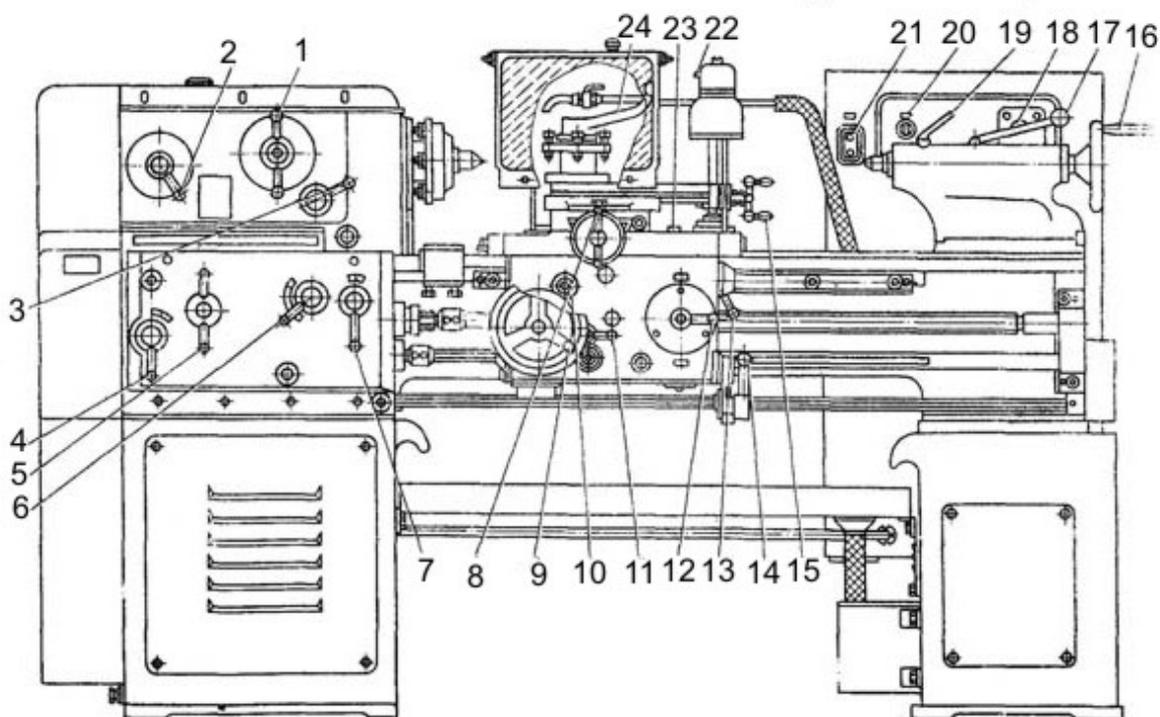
Узлы управления токарно-винторезного станка модели 1М61: 1 – Рукоятка установки чисел оборотов шпинделя; 2 – Рукоятка установки нормального или увеличенного шага резьбы и реверсирования вращения ходового винта; 3 – Рукоятка установки чисел оборотов шпинделя (рукоятка перебора); 4 – Рукоятка установки типа резьбы или подачи; 5 – Рукоятка установки величины подачи или резьбы; 6 – Рукоятка установки шага резьбы и подачи; 7 – Рукоятка включения ходового винта или ходового вала; 8 – Рукоятка поперечного перемещения суппорта; 9 – Маховик продольного
